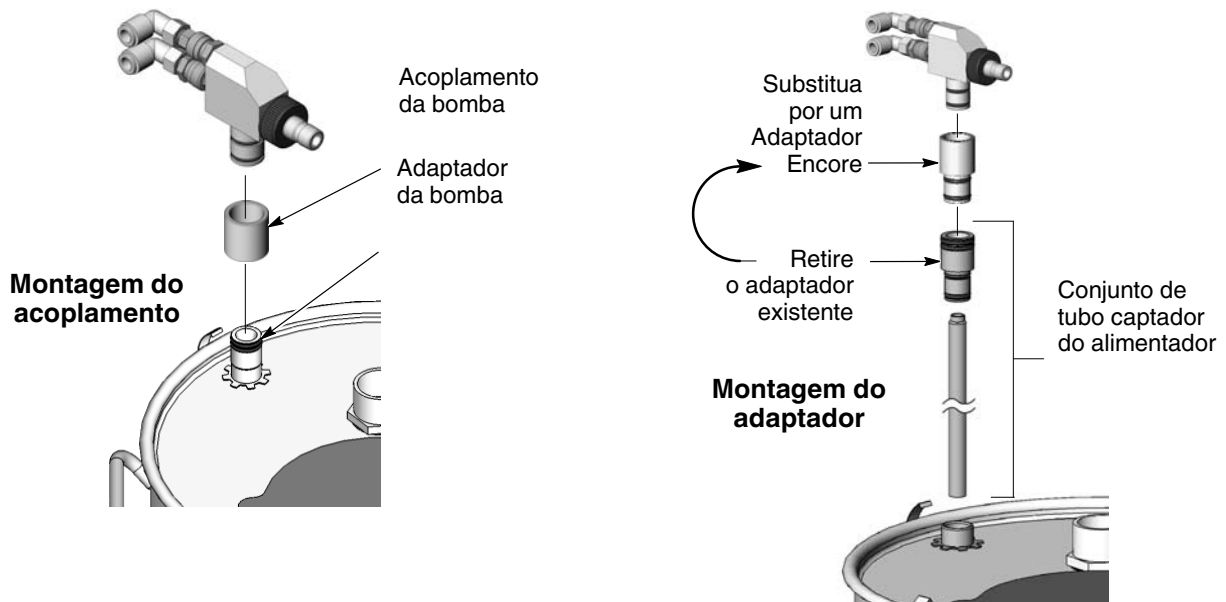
União da bomba com kit adaptador ou acoplamento em alimentadores HR ou NHR
